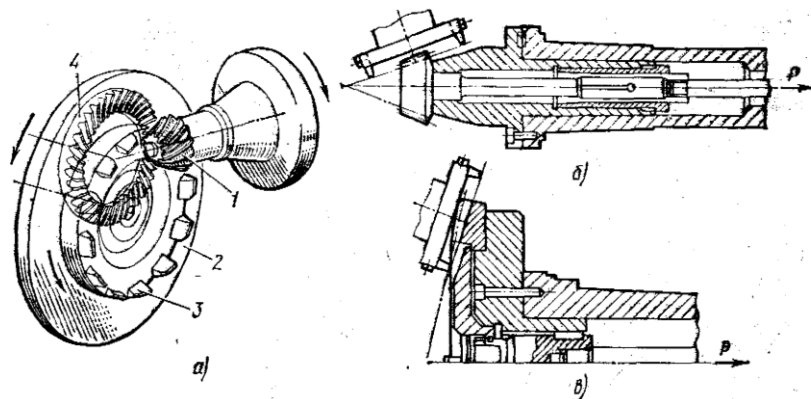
Схема нарізання кругових зубів конічних коліс за методом обкатування різцевими головками, розташування заготовки та схема нарізання різцевої головки (а), схема нарізання колеса – вала (б), схема нарізання плоского колеса (в)
